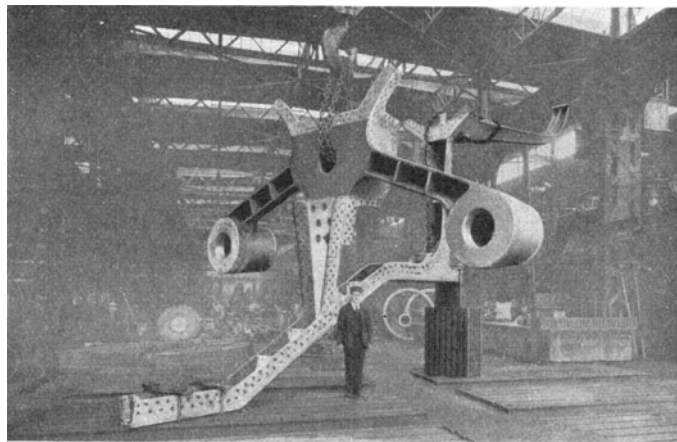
Stahlguß-Hinterstevan mit einteiligem Wellenträger, ebenfalls aus Stahlguß. Gewicht 20400 kg.
